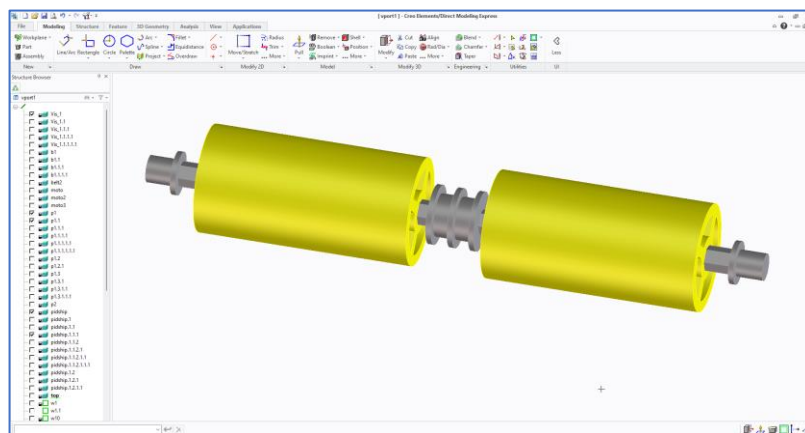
Зібрана конструкція з пари роликів та опорними підшипниками ковзання
